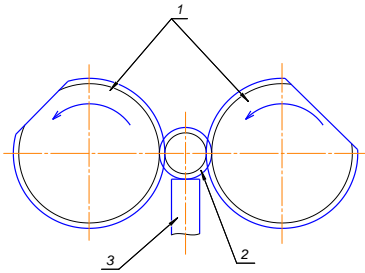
Накочування затильованими роликами: 1 – затильовані різьбові ролики, що обертаються; 2 - оброблювана деталь; 3– ніж
